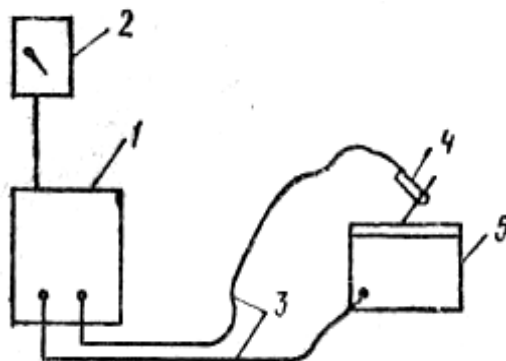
Зварювальний пост для ручного дугового зварювання: 1 – джерело живлення; 2 – пусковий апарат; 3 – зварювальні проводи; 4 – електродотримач; 5 – робоче місце зварника (зварювальна деталь)
